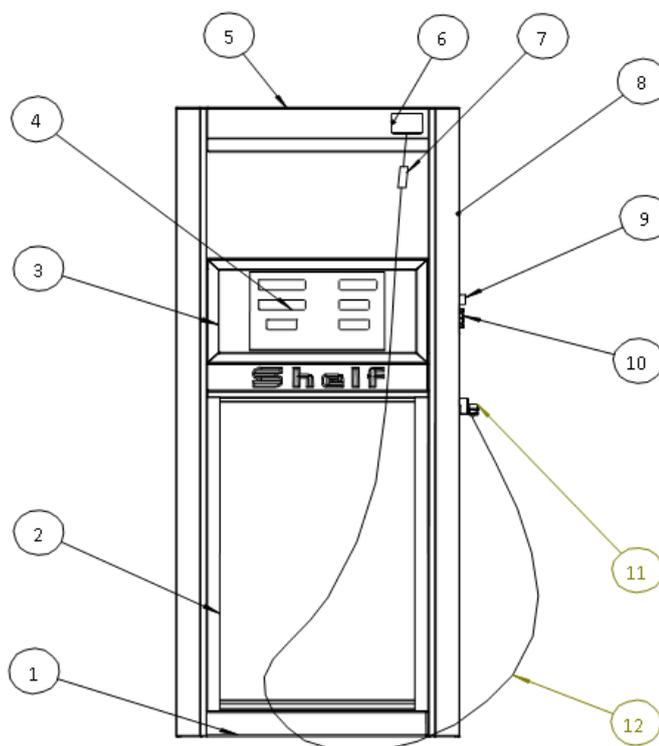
Внешний вид газонаполнительной колонки
